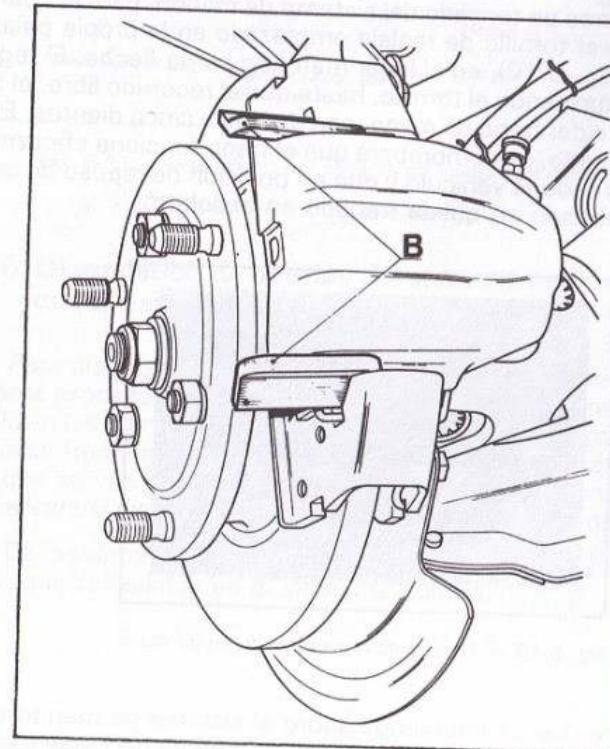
Proceso de desmontaje de la pinza de frenos.
